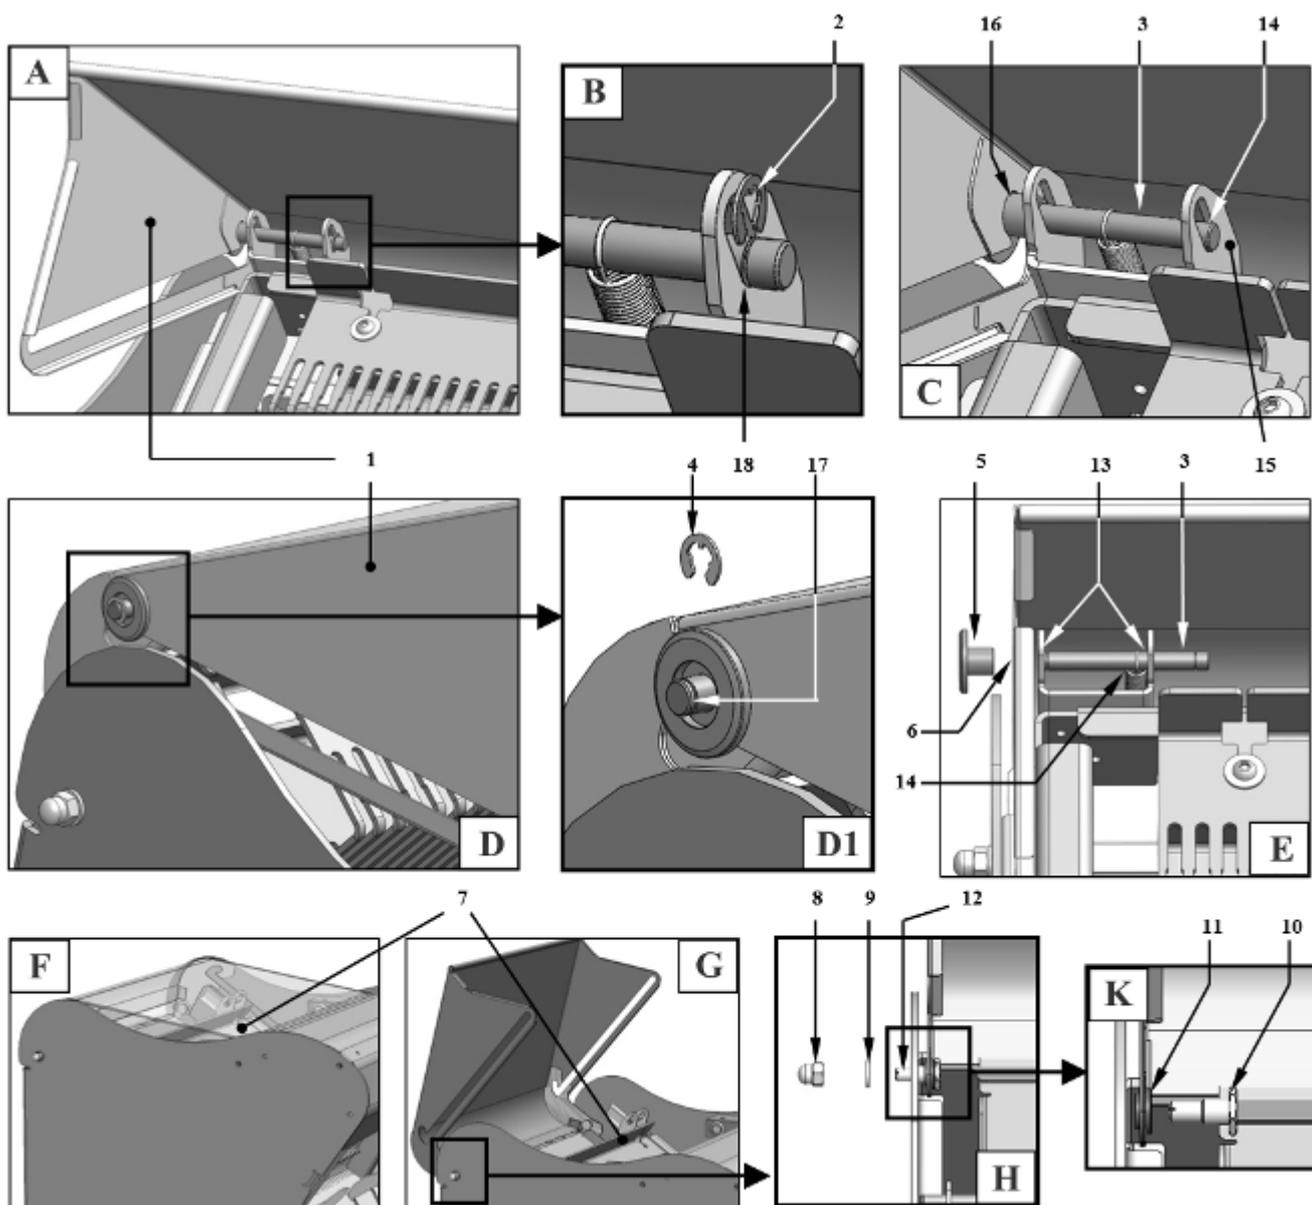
Демонтаж/установка верхнего защитного устройства
